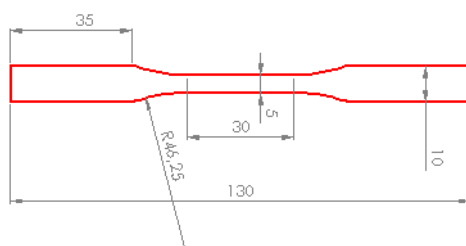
dimensions (en millimètres) d’une éprouvette en époxy
